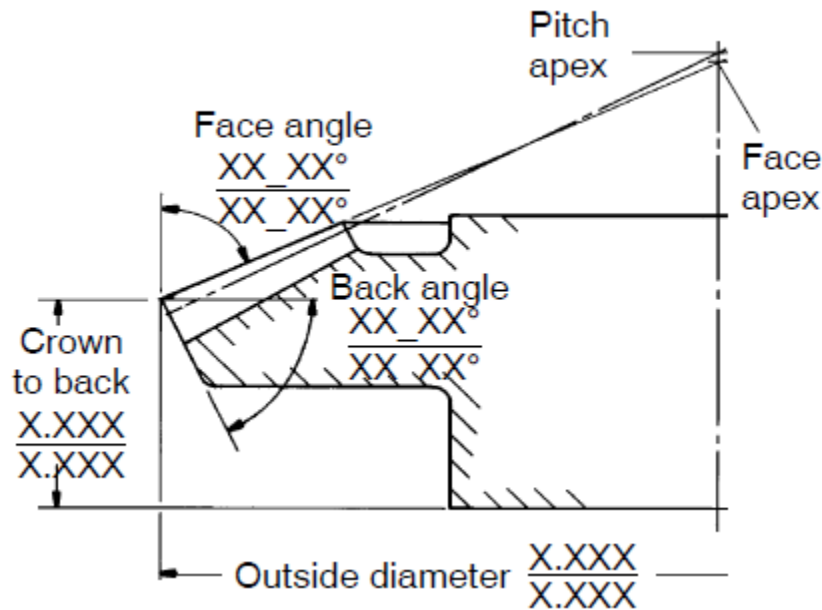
Especificación de blancos para las tolerancias de engranajes cónicos
